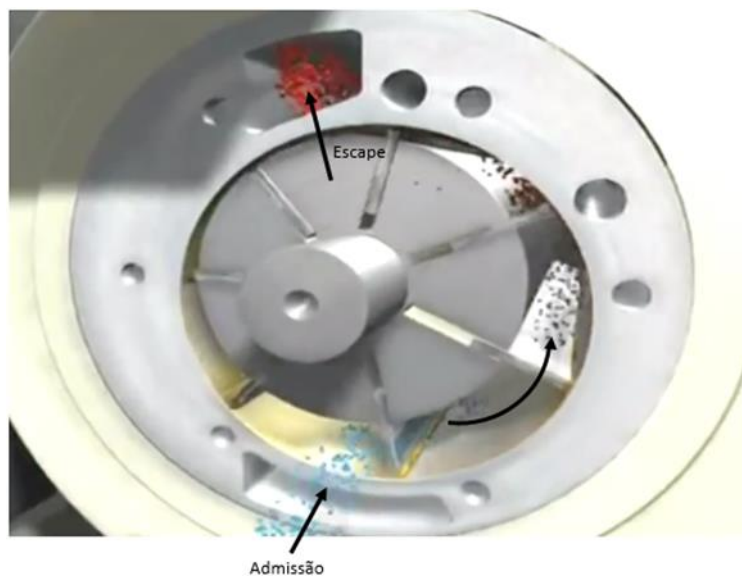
Compressor rotativo de alhetas, adaptado [11].
